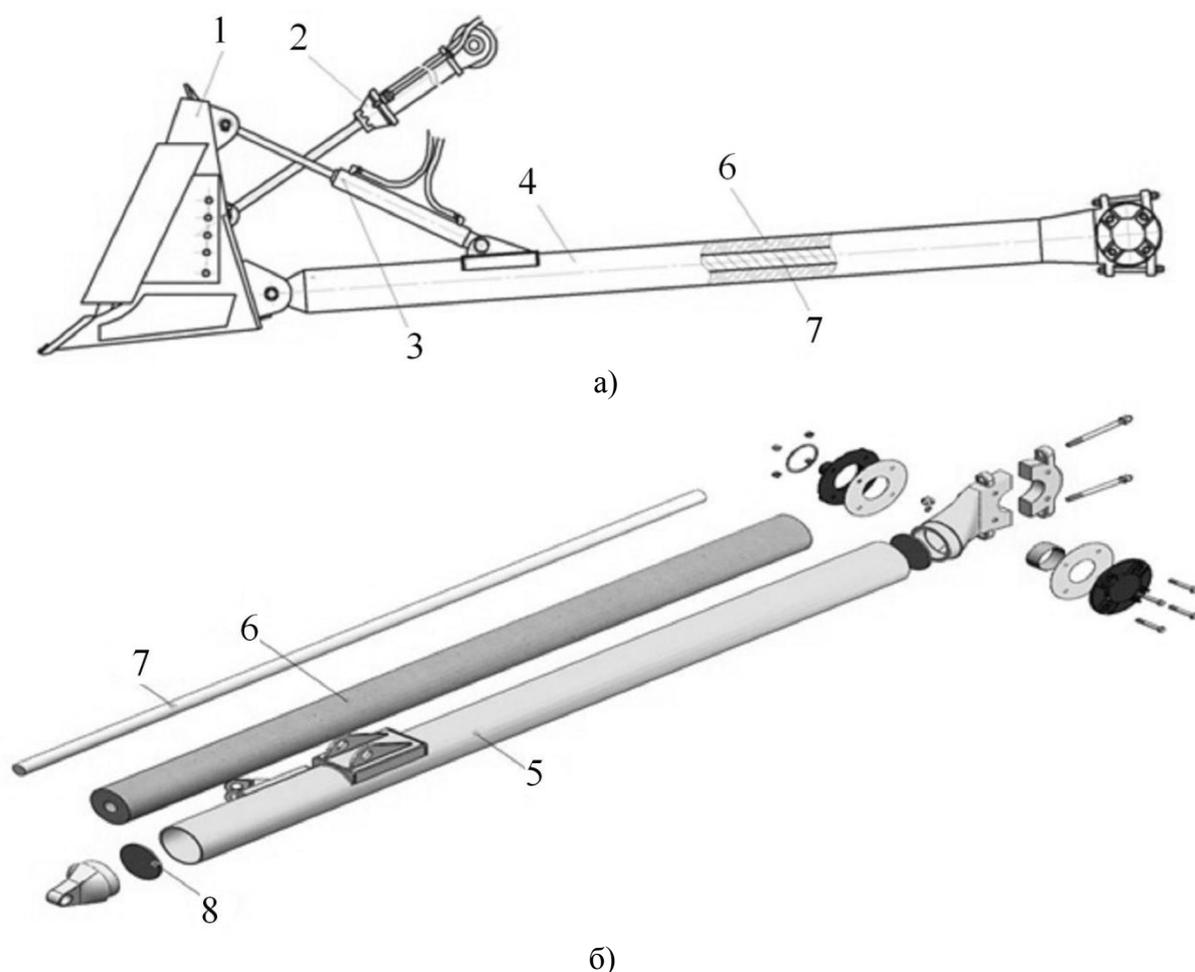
Бульдозерное рабочее оборудование с повышенной прочностью толкающего бруса: а) – вид общий; б) - изометрический вид толкающего бруса в разнесенном состоянии: 1 - отвал; 2 - гидроцилиндр подъема; 3 - гидроцилиндр изменения угла наклона отвала; 4 - толкающий брус; 5 - труба круглого сечения; 6 - наполнитель; 7 - арматурный стержень; 8 - стопорная крышка.
